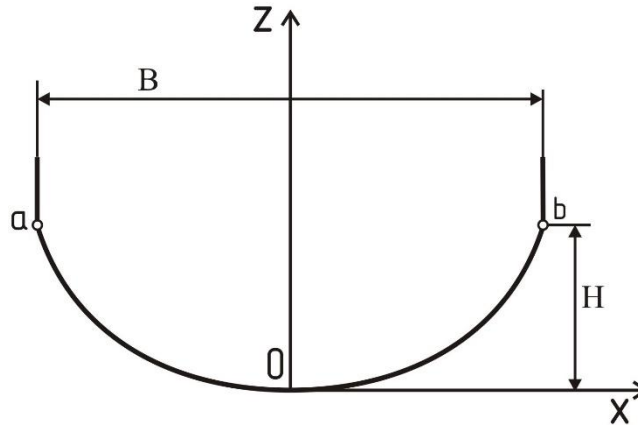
Схема для визначення параметрів форми поверхні криволінійної частини скоби.
